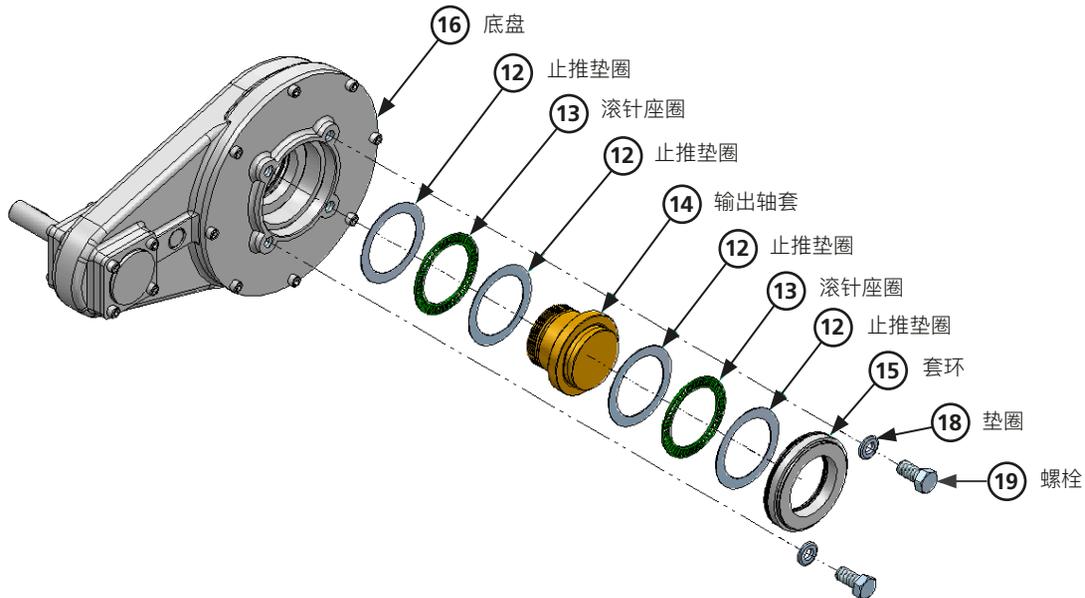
锥齿轮箱和正齿轮箱输出轴套组件
